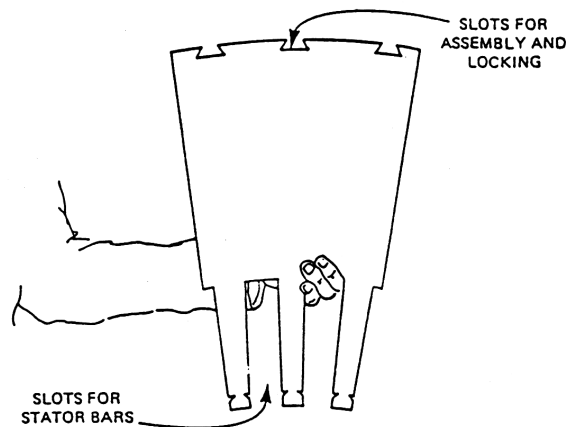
수소냉각방식 발전기의 Core Mounting 단면도
